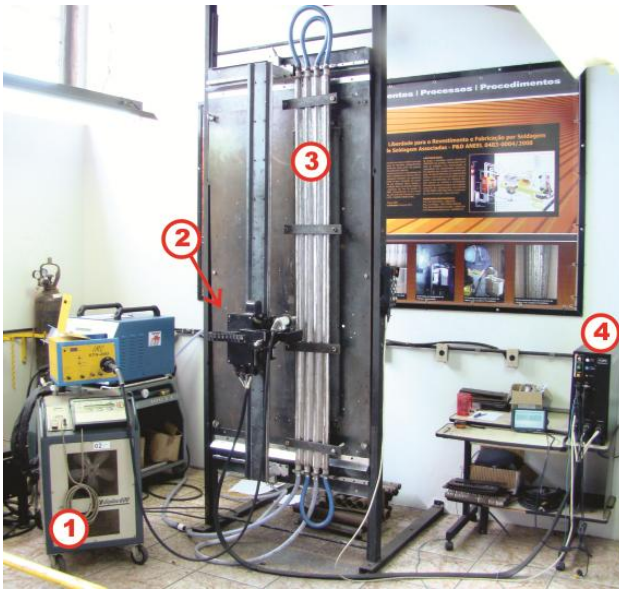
Bancada inicial para revestimento robotizado de painel tubular. Em (1) Fonte de soldagem, (2) Robô CNC, (3) Tubos de paredes de caldeira e (4) Gabinete de controle com IHM
